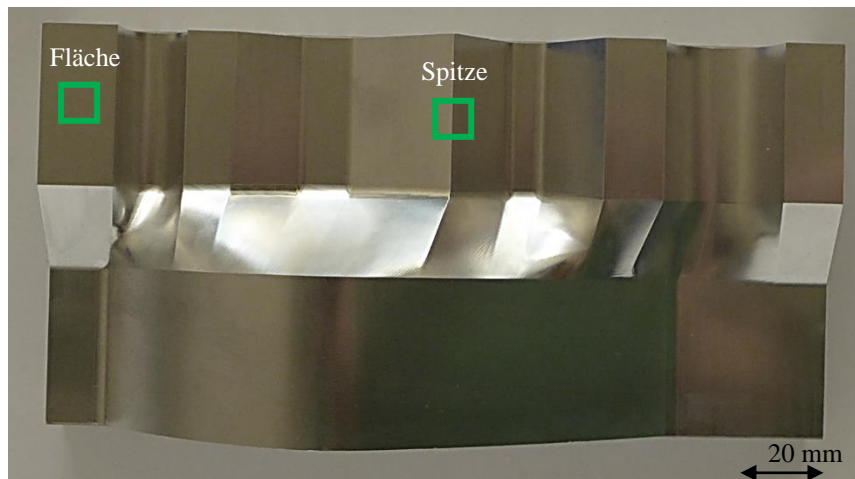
Fräsbauteil für die Untersuchung der Z-Schlitten im Praxistest
